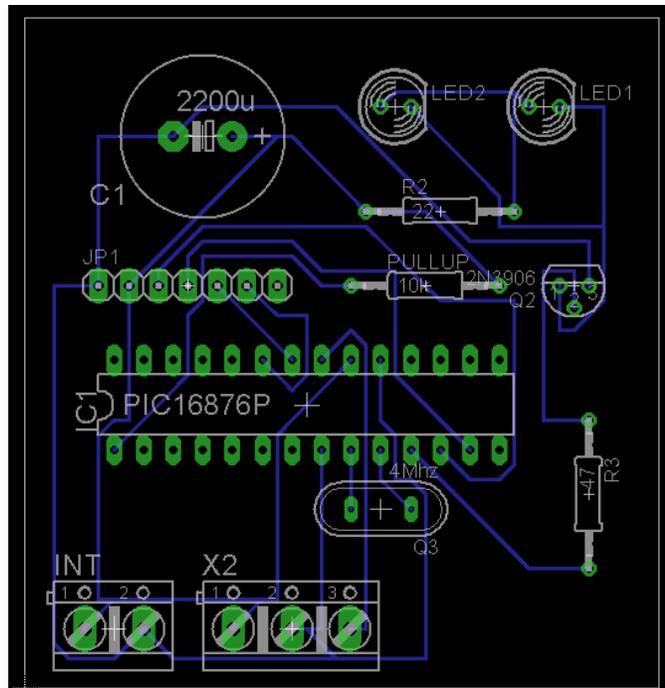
Diseño en EAGLE de la PCB del control del aire acondicionado y la videocámara.
